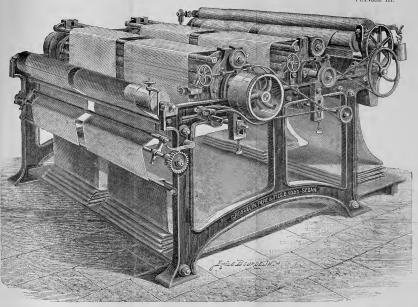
Machine à lainer à deux tambours, de MM. Grosselin père et fils
